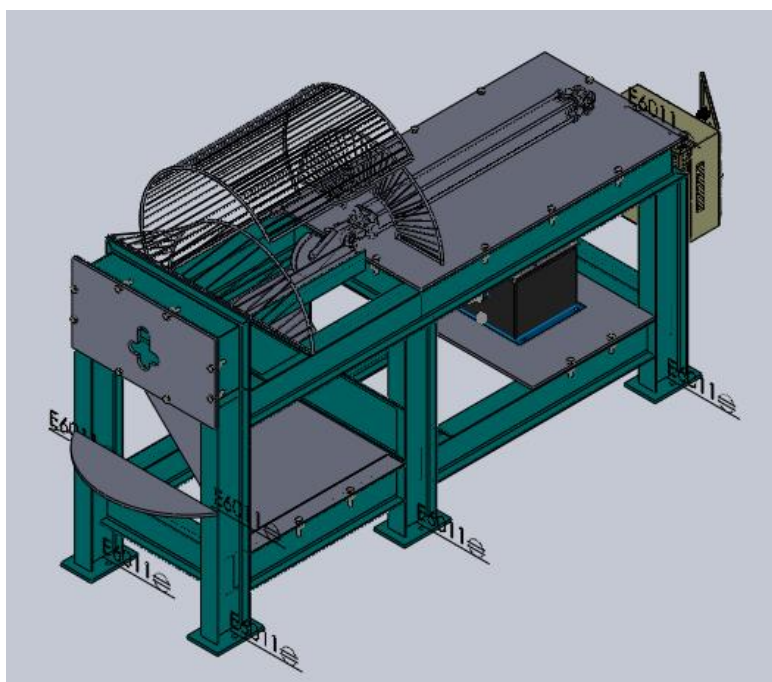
Diseño CAD del Prototipo de Máquina para la Extracción del Aro de Talón
